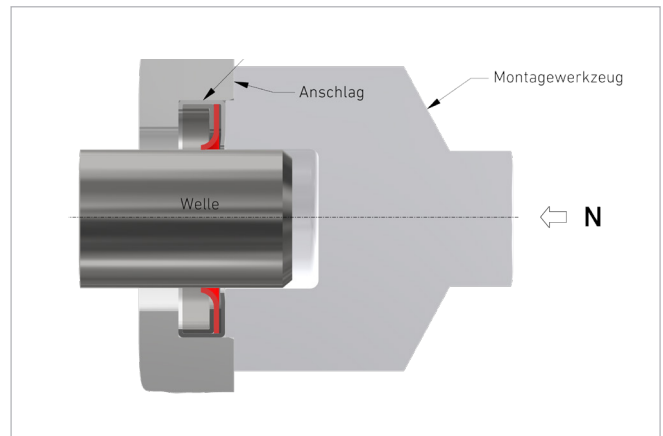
Montagehilfe für Radialwellendichtungen - Anschlag an Gehäusefläche
